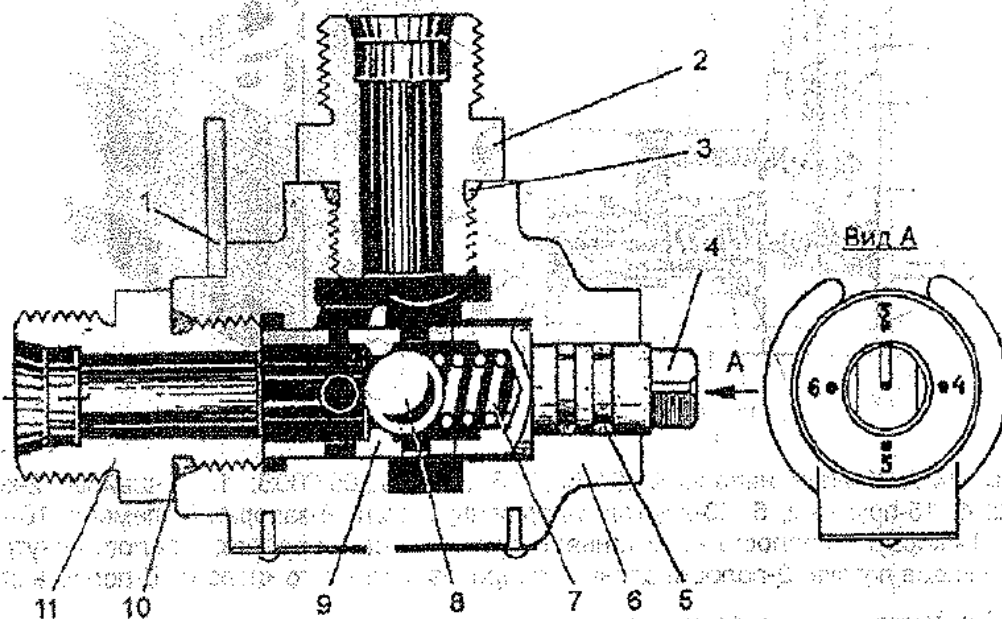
Клапан дросселирующий настраиваемый КДН 00.000-06: 1-кронштейн; 2, 11-штуцеры; 3, 5-кольца уплотнительные; 4-шпindel; 6-корпус; 7-пружина; 8-шарик; 9-золотник дроссельный
